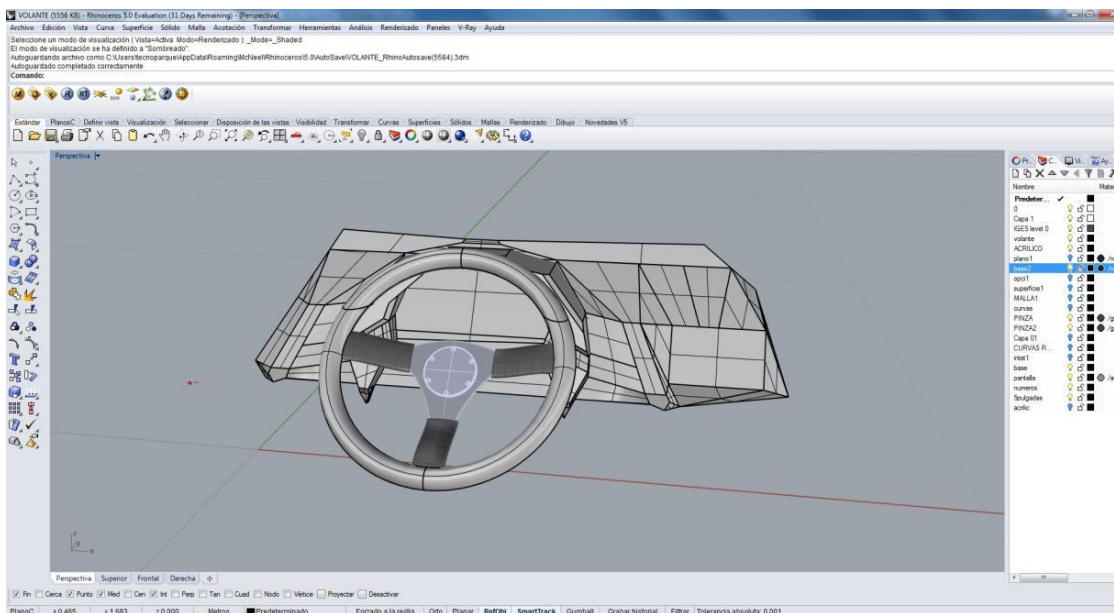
Alternativa para panel de mandos. Elaborado por Johandra Mantilla.
